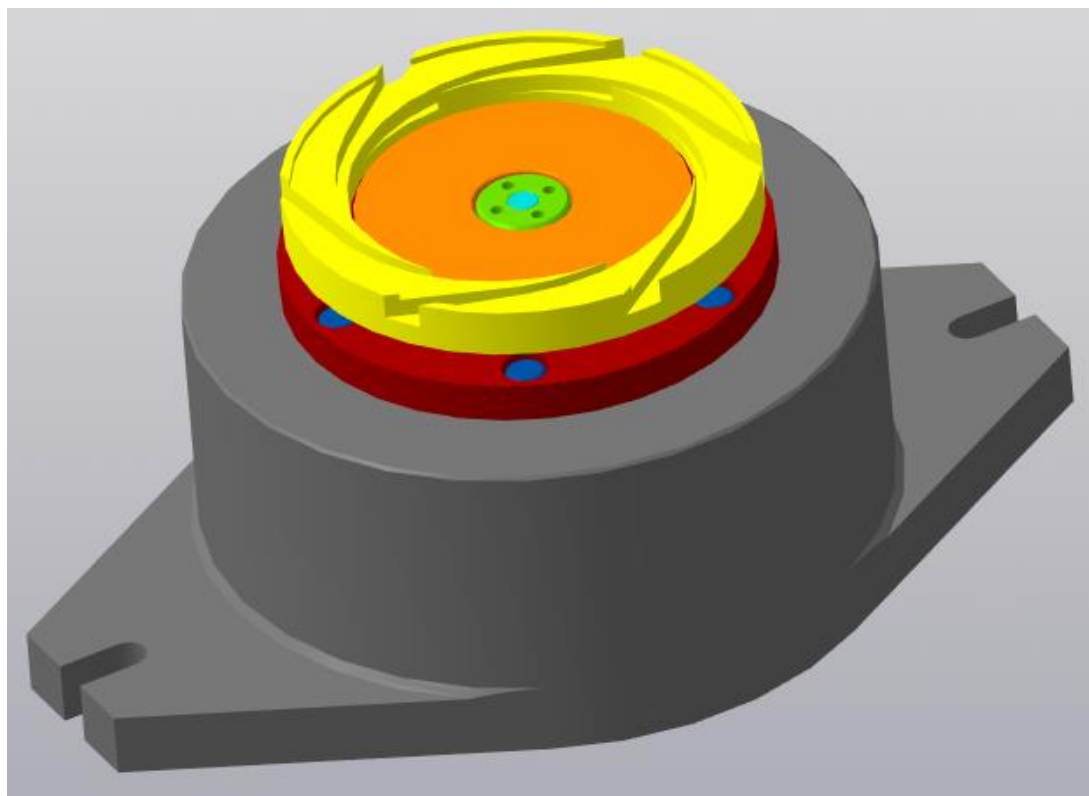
Спроектований верстатний пристрій та закріплена деталь
